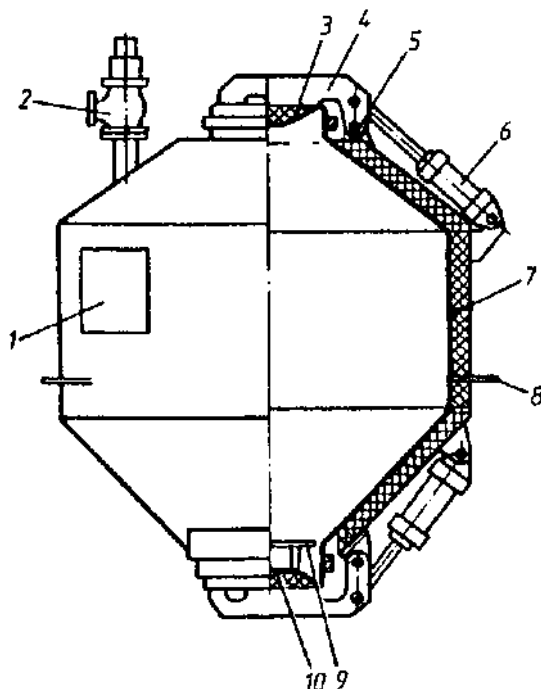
Вертикальний безкорзинний автоклав Н10-ІАВ: 1 – кишень-камера; 2 – запобіжний клапан; 3, 10 – верхня і нижня кришки; 4 – важіль; 5 – вісь; 6 – пневмоциліндр; 7 – корпус; 8 – лапи
